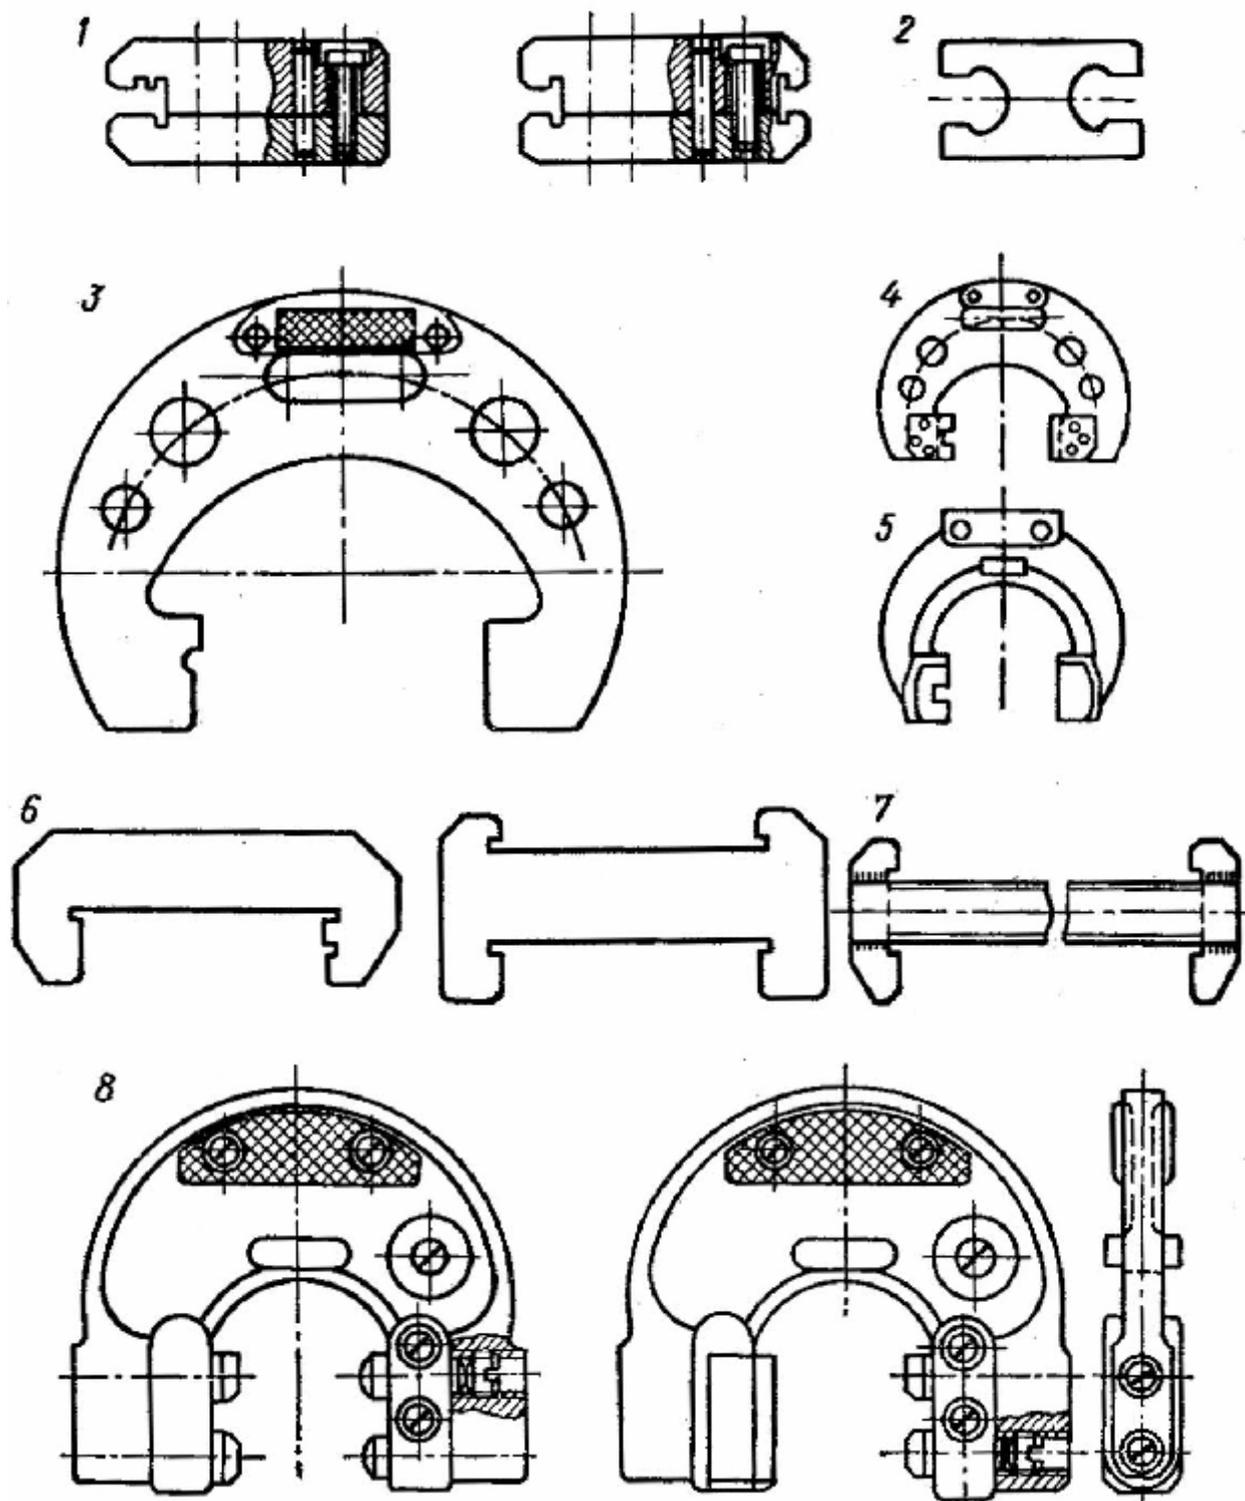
Конструкция и типы калибров для контроля размеров наружных цилиндрических поверхностей
